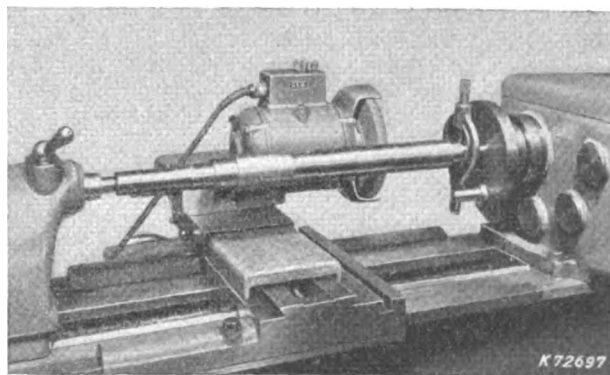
Schleifen einer Welle mittels Supportschleifmaschine auf einer Drehbank.
